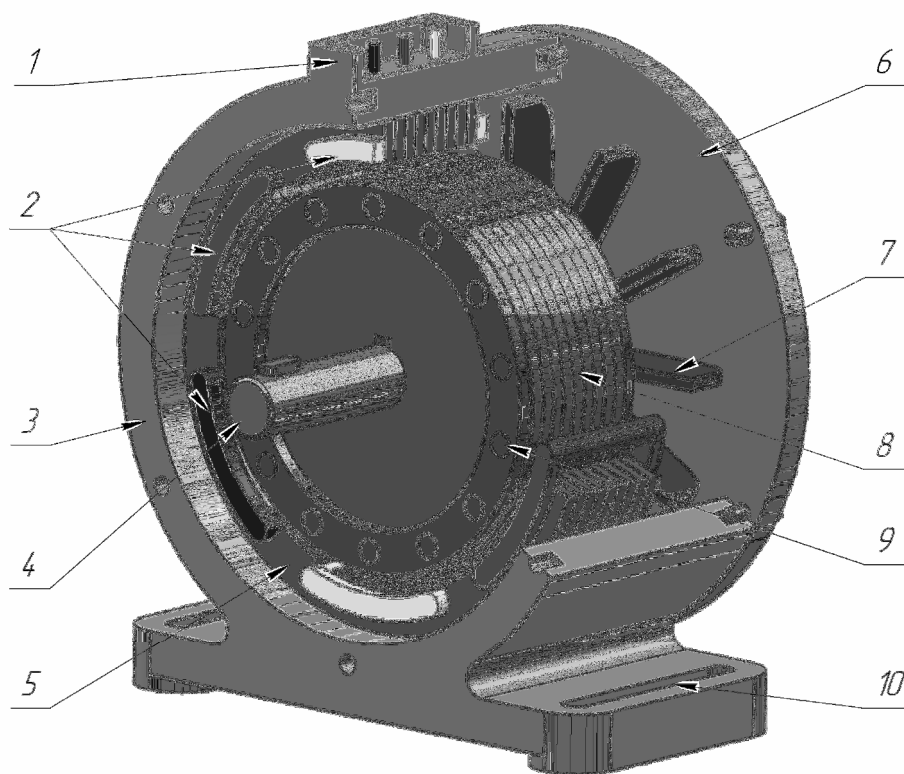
Конструкция асинхронного электродвигателя: 1 – клеммник; 2 – трехфазная обмотка; 3 – корпус; 4 – вал; 5 – магнитопровод статора; 6 – крышка с подшипниковым узлом; 7 – вентилятор; 8 – магнитопровод ротора; 9 – короткозамкнутая обмотка; 10 – монтажные отверстия корпуса
